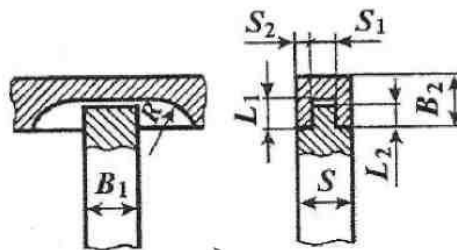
Схема одноелементного кутового з'єднання брусккових деталей, серединне на шип ненаскрізний в паз (УС-2)
